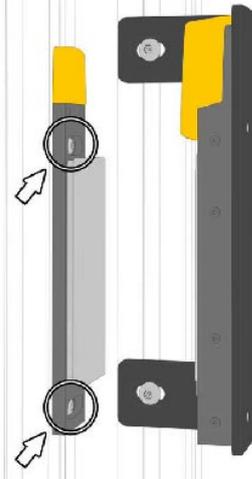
Ankerplatte am Profil der Schiebetüre anbringen, zur Prozesszuhaltung ausrichten und zur Prozesszuhaltung ausrichten. Schrauben M6 x 12 mm Torx festziehen.
